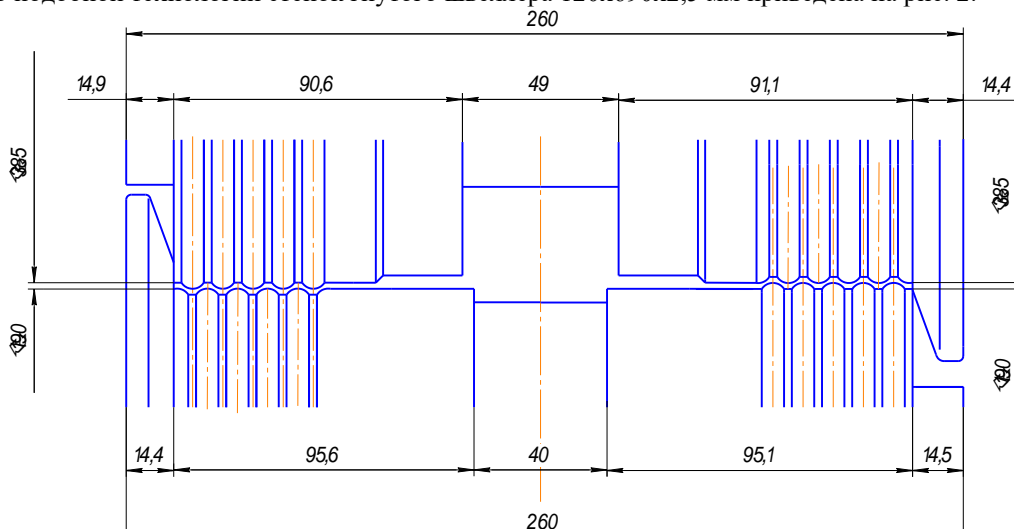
Калибровка валков клетки для формовки рифлений на стенках швеллера 120х60х2,5 мм
